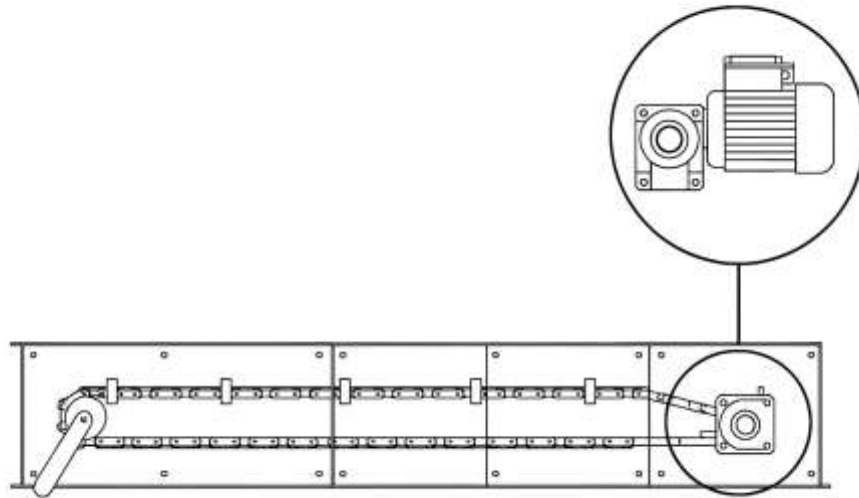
D motor pada conveyor FFB ini menampilkan bentuk conveyor yang akan digerakkan oleh motor FFB dan menunjukkan posisi letak motor pada bagian conveyor.
